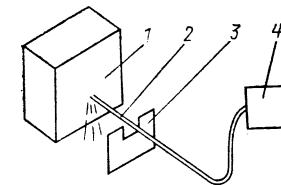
Принцип резки: 1 — заготовка; 2 — кислородное копье; 3 — экран; 4 — рама
